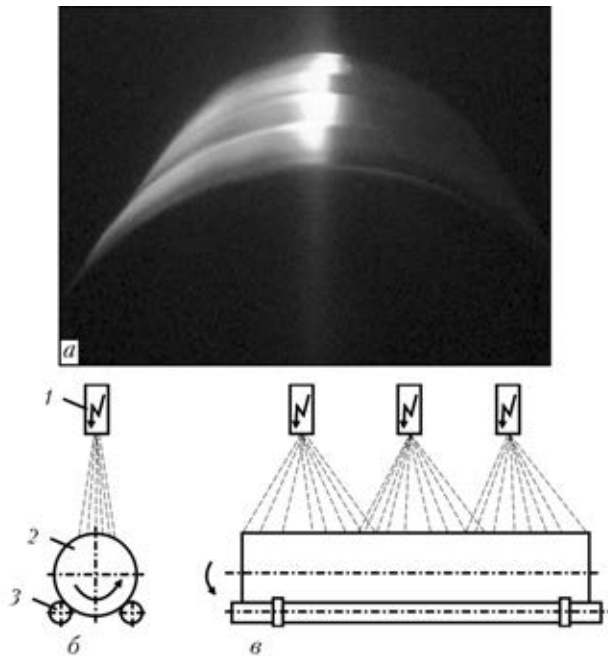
Процесс оплавления слитка цилиндрического сечения: *a* – внешний вид; *б* – схема; 1 – электронно-лучевая пушка; 2 – слиток; 3 – валки механизма вращения слитка
